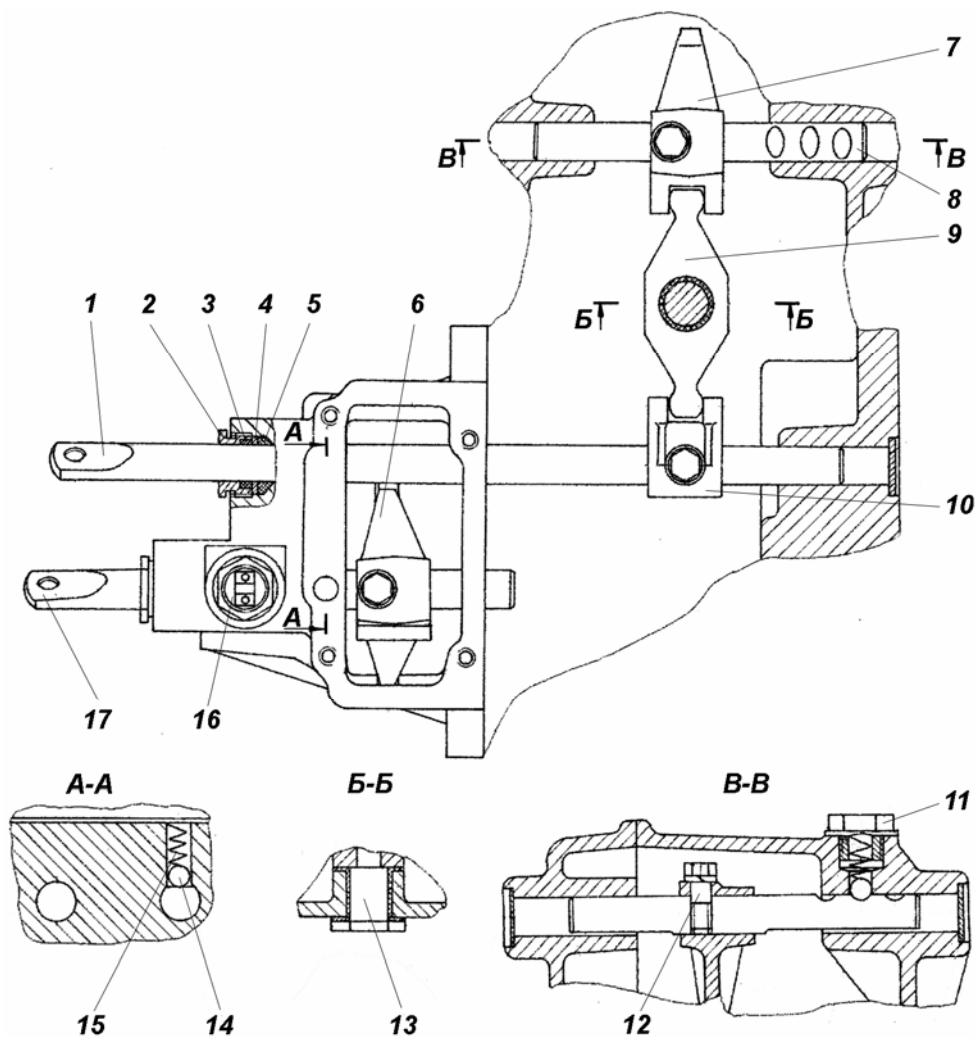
Механизм включения передач и блокировки дифференциала: 1 – промежуточный шток; 2 – гайка сальника штока; 3 – уплотнительное кольцо; 4 – шайба; 5 – сальник штока; 6 – вилка включения блокировки дифференциала; 7 – вилка включения передач; 8 – шток включения передач; 9 – промежуточный рычаг; 10 – головка штока; 11 – пробка; 12 – болт; 13 – ось промежуточного рычага; 14 – шарик фиксатора; 15 – пружина фиксатора; 16 – датчик включения блокировки дифференциала; 17 – шток включения блокировки дифференциала
